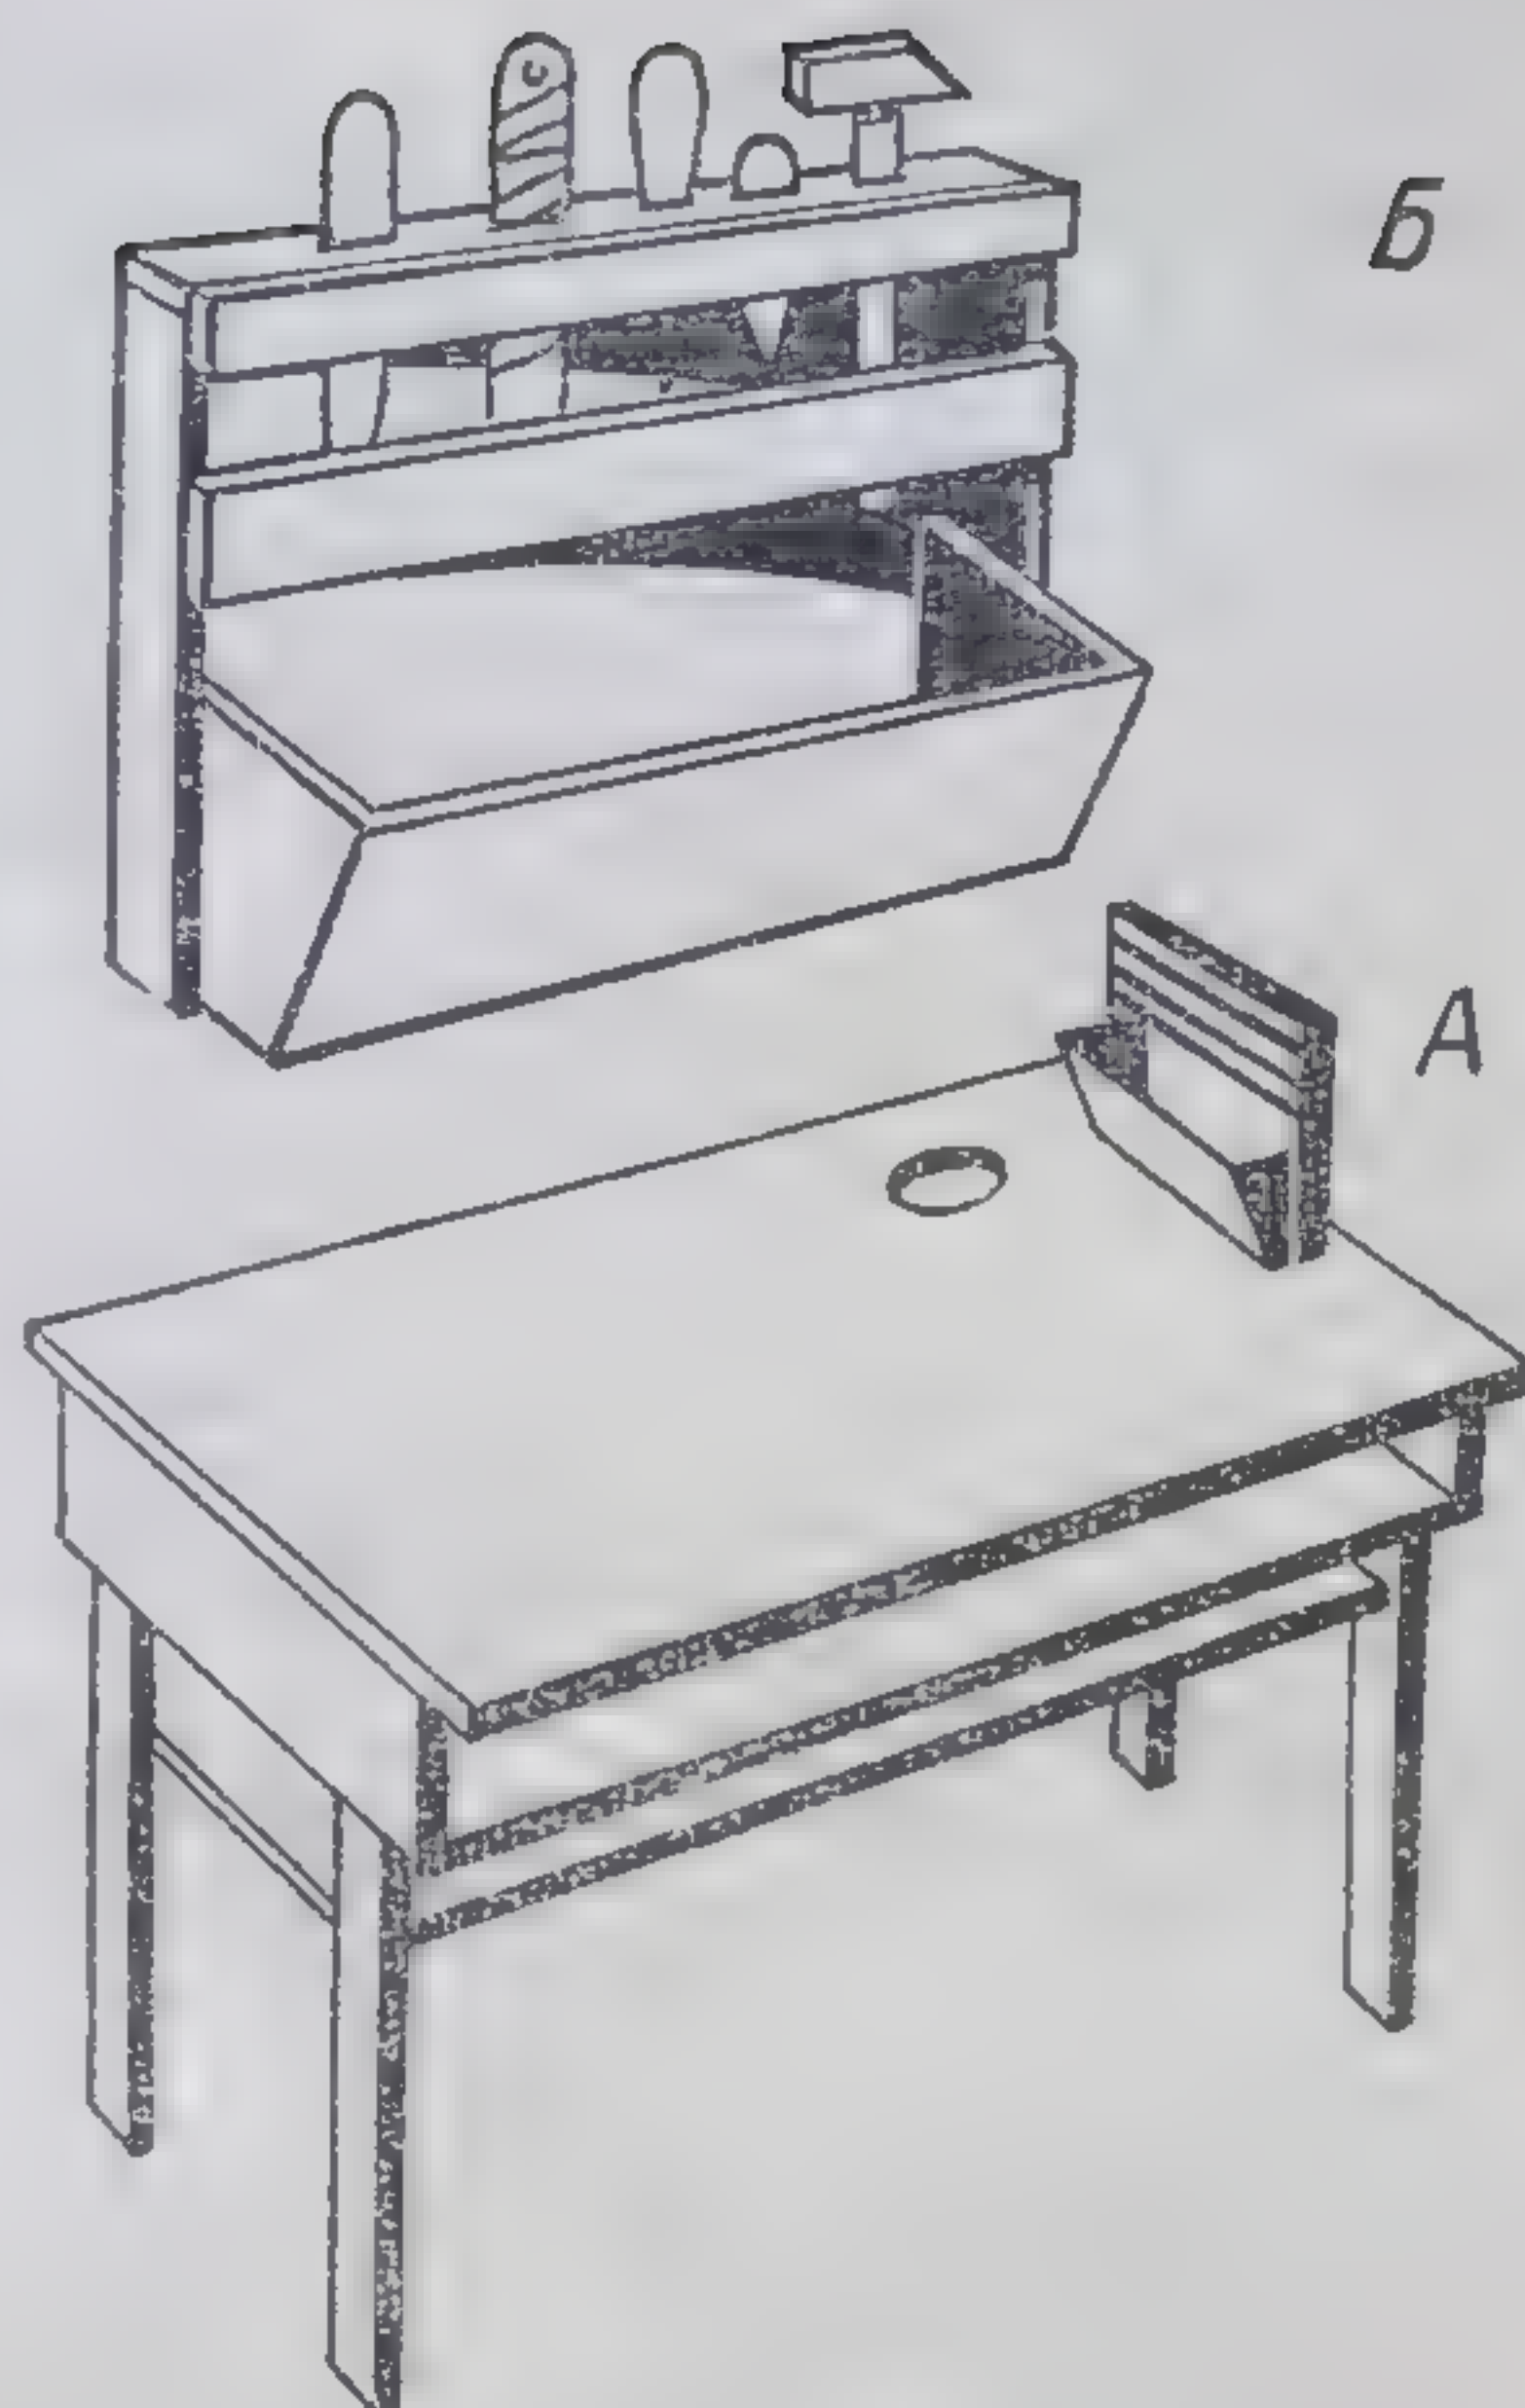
Стол для переплетных работ: А — вариант переоборудования ученического стола; Б — пенал для хранения инструментов
